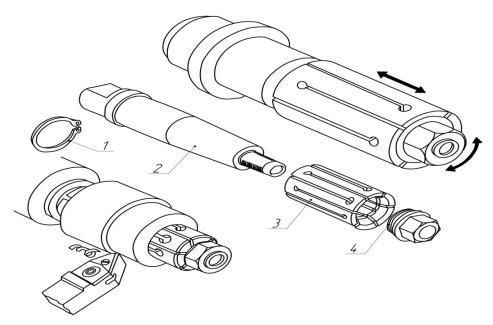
Центровая разжимная оправка с упорным кольцом: 1 — разжимное упорное кольцо; 2 — оправка; 3 — цанга; 4 — гайка
